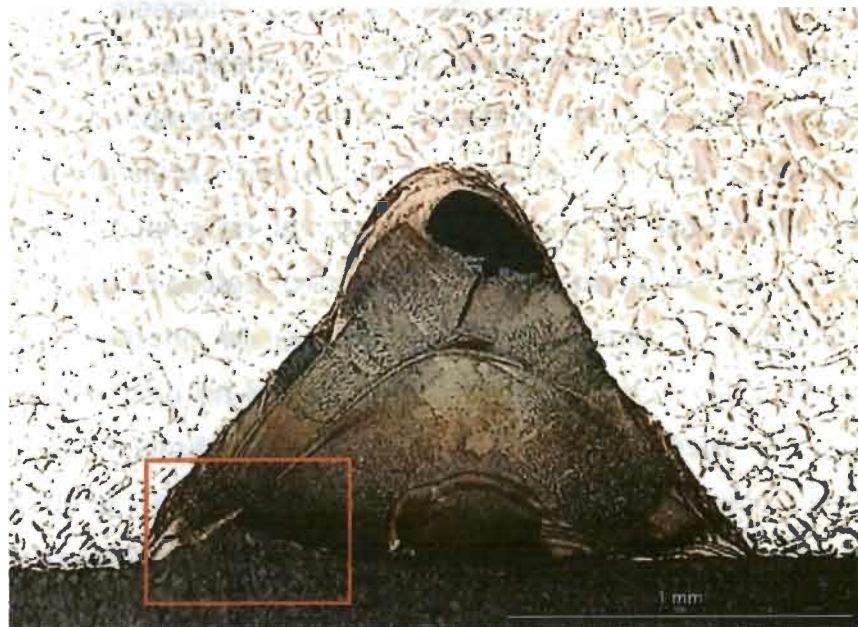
Socavamiento en una soldadura láser.
